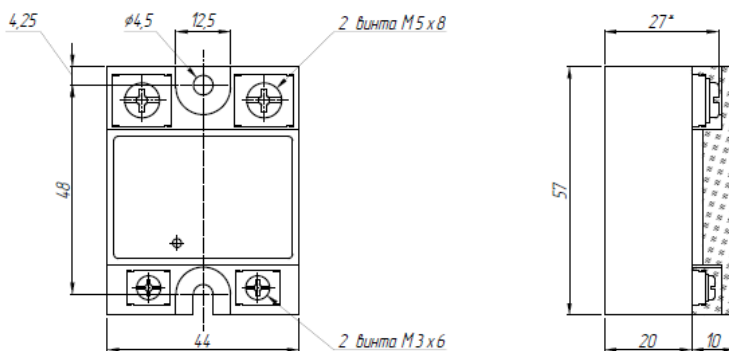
габаритные и установочные размеры ТТП серий HD-●●44.VA, HD-●●25.LA
